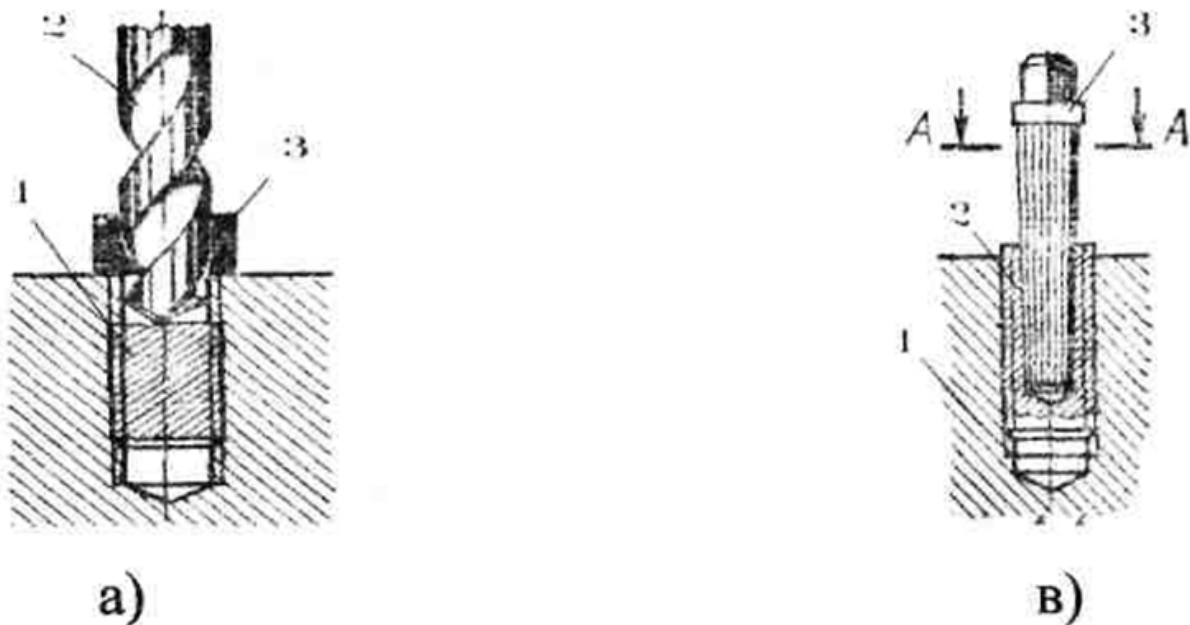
Видалення обірваної шпильки: а) висвердлювання по кондукторній втулці: 1- шпилька; 2- свердло; 3- кондукторна втулка; б) викручування шпильки циліндричним екстрактором: 1- циліндричний екстрактор; 2- шпилька; 3- деталь.
